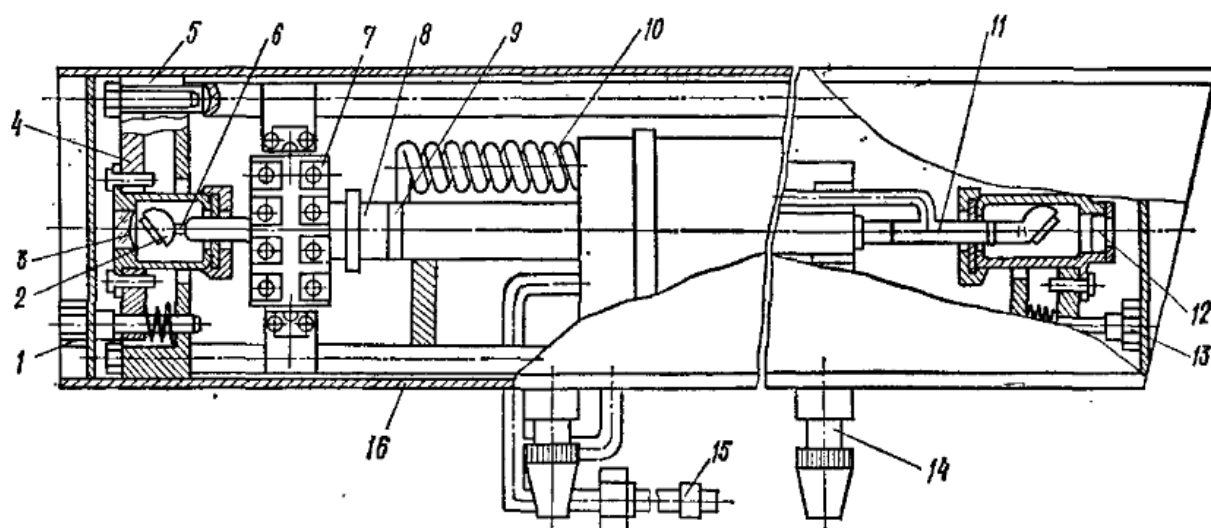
Схема конструкції випромінювача аргонного лазера типу ЛГ-106: 1,13 – юстувальні гвинти; 2 – вікно трубки; 3 – сферичне дзеркало; 4 – юстировочна головка; 5 - кронштейн; 6 – капіляр газорозрядної трубки; 7 – клемна колодка; 8 – магніт; 9 – катод; 10 – спіраль обвідного каналу; 11 – анод; 12 – вихідне дзеркало; 14 – горизонтуюча підставка; 15 – штуцер системи охолодження; 16 - кожух
